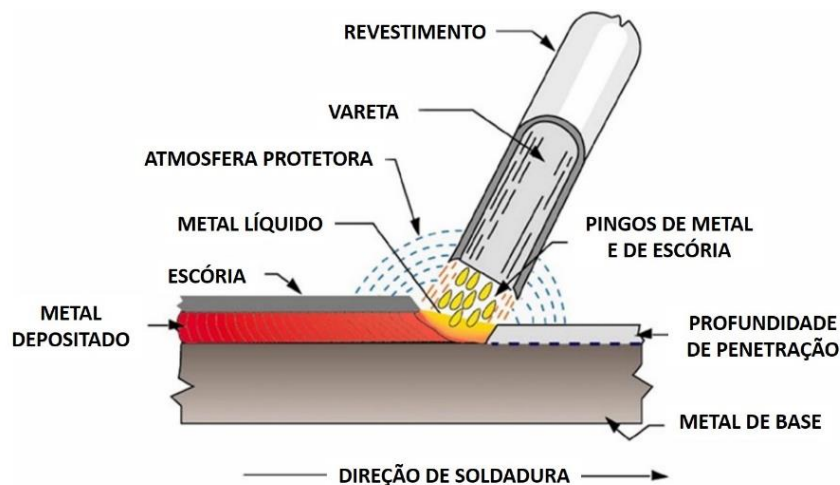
Esquema de soldadura por eletrodo revestido (adaptado de [17])
